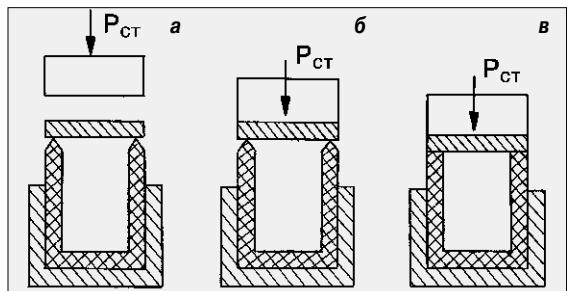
Схема сварки деталей с разделкой кромки
